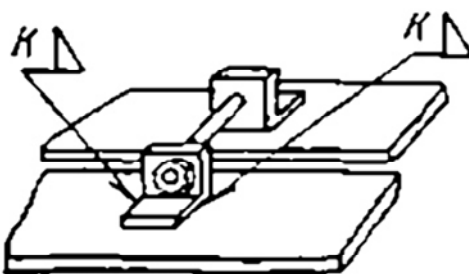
Стяжка с болтом и приваренными угольниками для сварки крупных конструкций из листового проката
